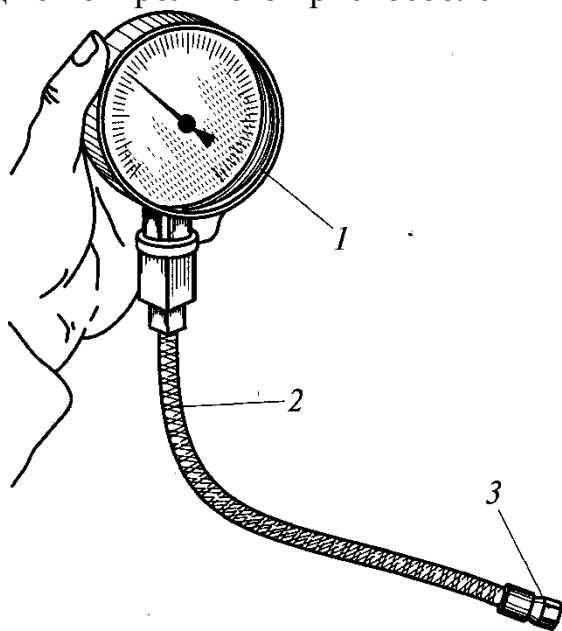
Контрольное приспособление КИ-13936: 1 – манометр; 2 – соединительный шланг; 3 – накидная гайка
